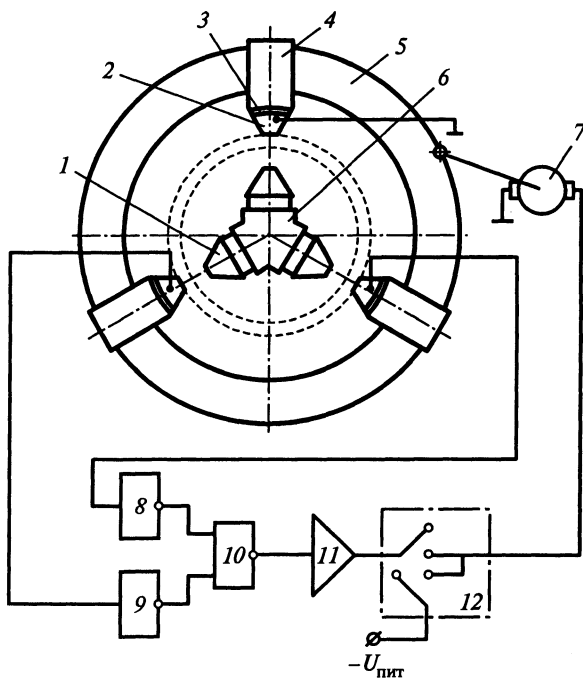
Устройство крепления тонкостенных цилиндрических заготовок:
